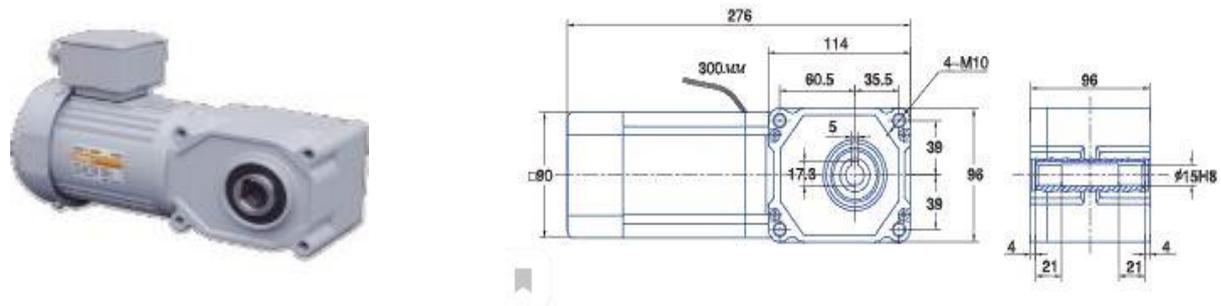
Мотор-редуктор серии HG-90 габаритные размеры
